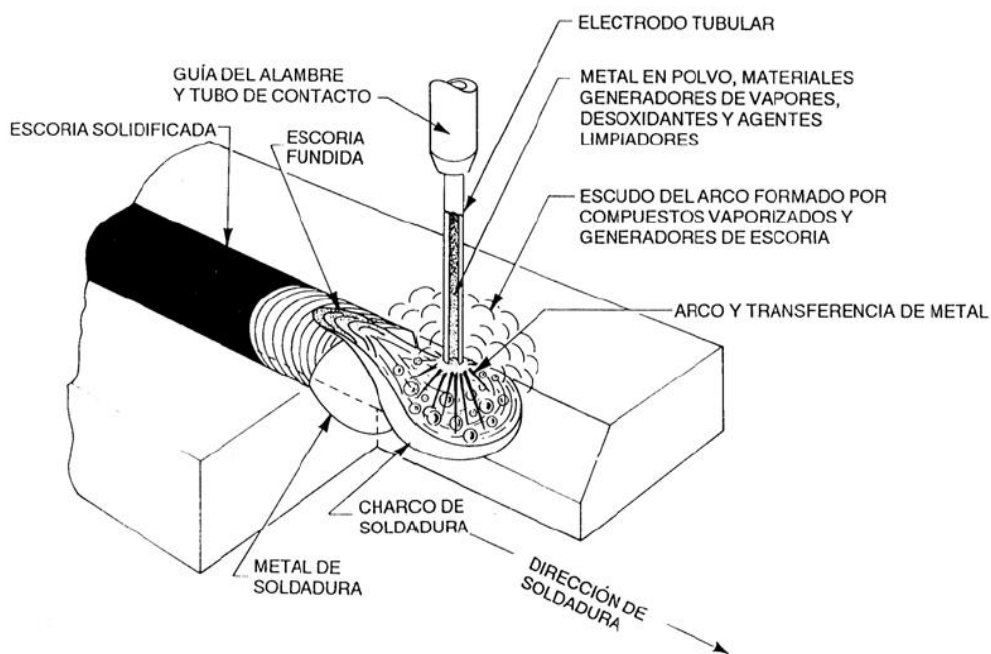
Soldadura por arco con núcleo de fundente protegida
